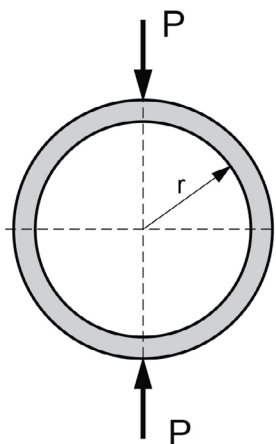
Схема нагружения кольцевой заготовки двумя радиальными усилиями при правке
